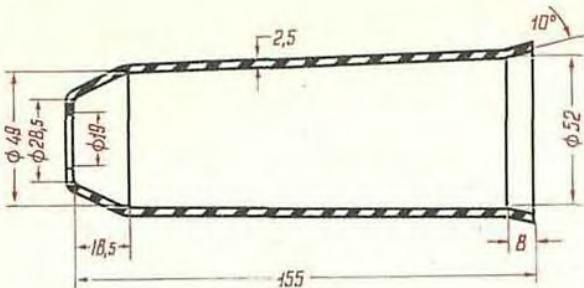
Защитный резиновый колпак переднего амортизатора.
